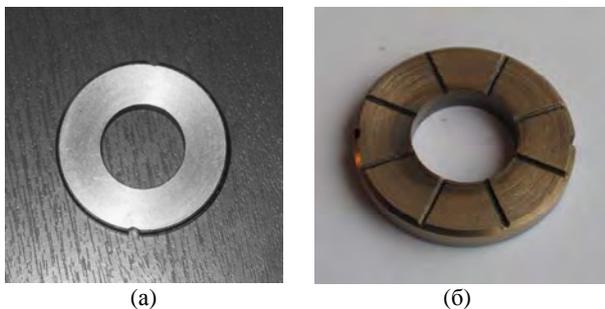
Внешний вид образцов: (а) – образец с ПКХП; (б) – образец с накладками из медного композита МК-5.
